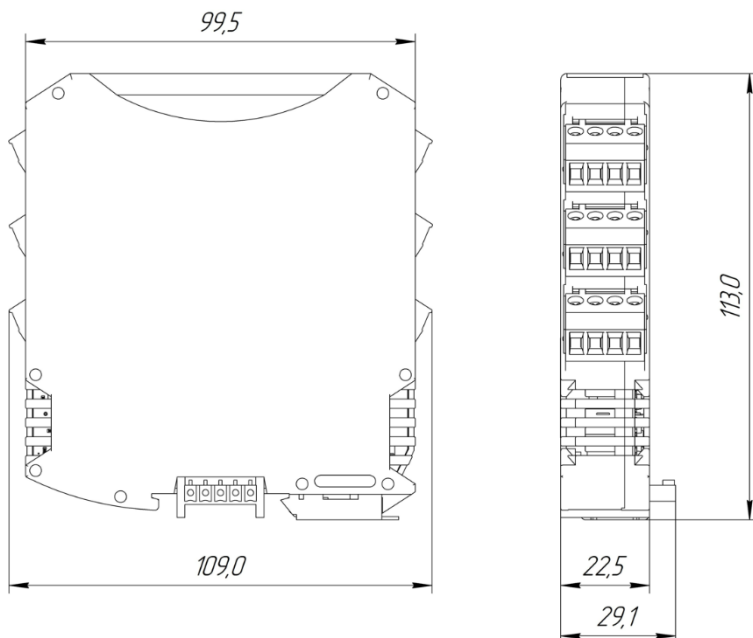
Габаритный чертеж преобразователя в стандартном корпусе
